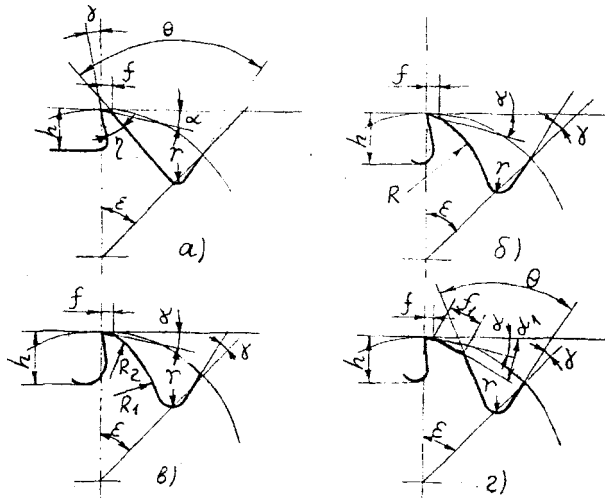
Формы зубьев и канавок цилиндрических фрез
